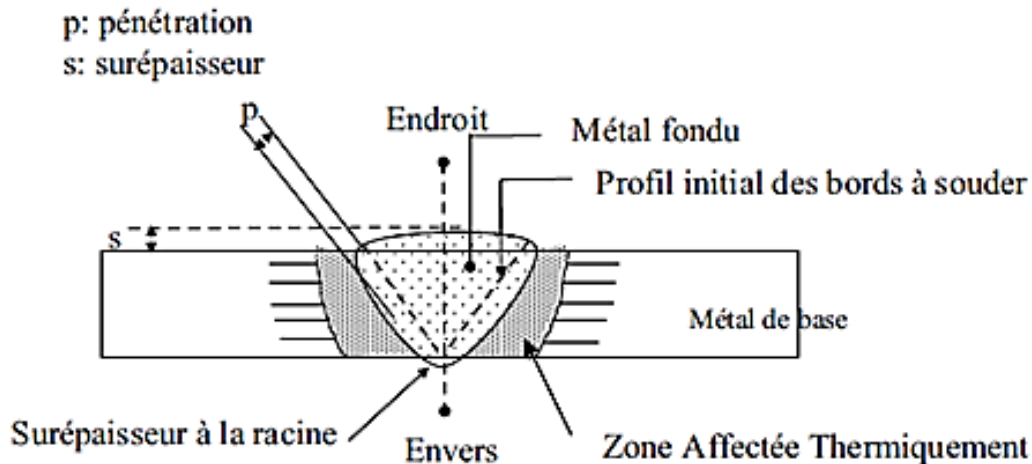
Soudure bout à bout sur chanfrein en V.
